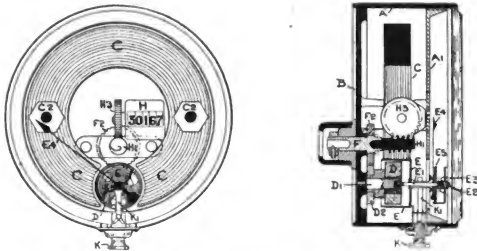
Innen-Ansichten des Oratze-Geschwindigkeitsmessers.
